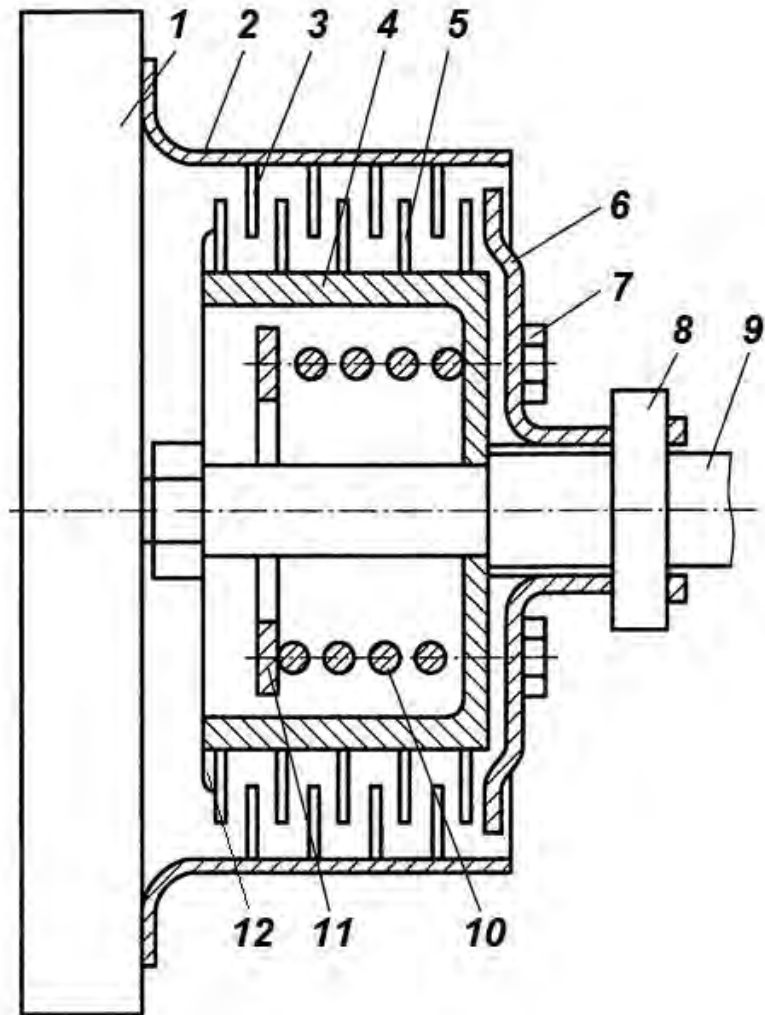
Принципова схема багатодискового зчеплення [6]:
